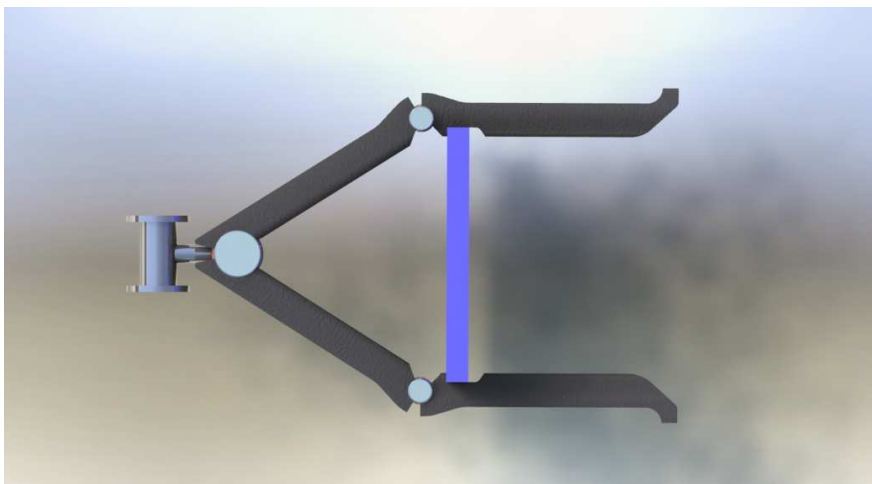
oggetto rettangolare in presa (modo 2), vista dall'alto
